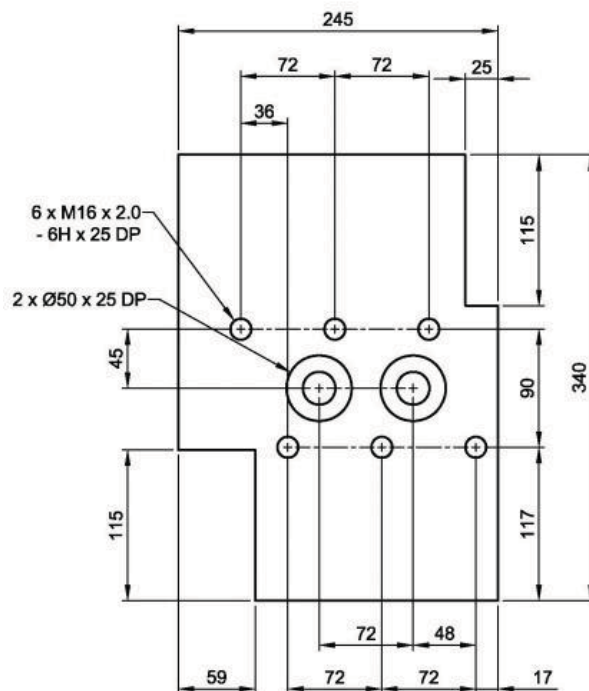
Dimensions des trous de fixation de la plaque de fond de l'USV de la barre de plongée avant
